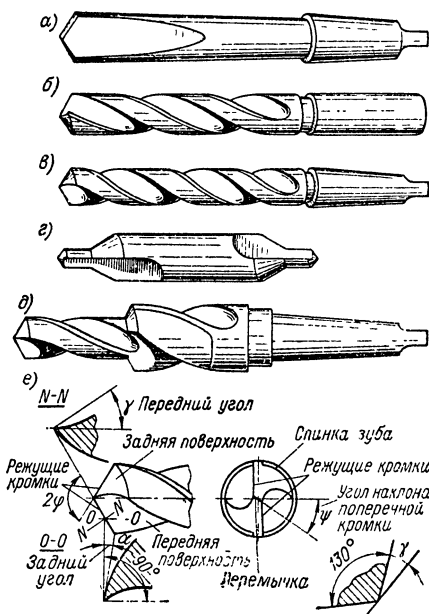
Конструкции сверл: а — перовые; б — спиральные с цилиндрическим хвостовиком; в — спиральные с коническим хвостовиком; г — центровые; д — комбинированное сверло-зенкер; е — геометрия заточки спирального сверла
